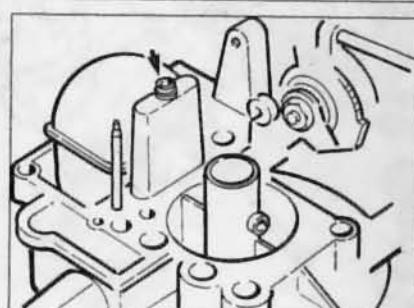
Верхний корпус карбюратора 1В3 (перевернутый), расположение главного жиклера - отмечено стрелкой (Глава 10)
